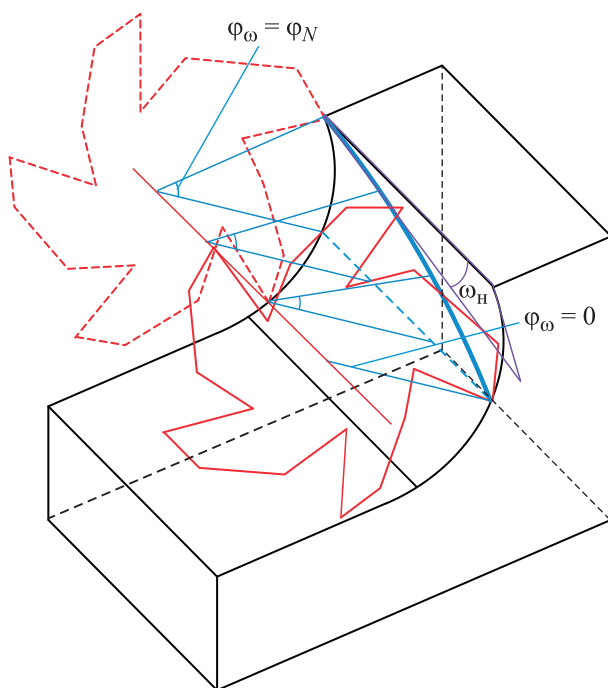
Обработка детали цилиндрической фрезой с винтовыми зубьями
